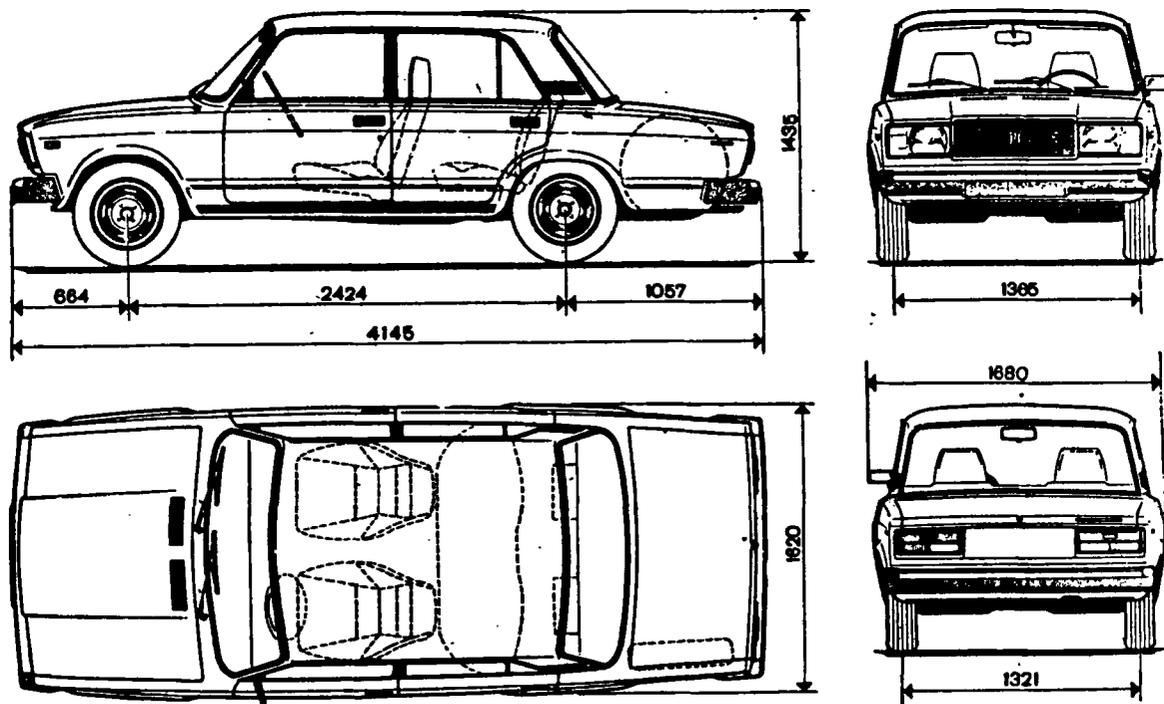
Основные габаритные размеры автомобиля ВАЗ-2107
